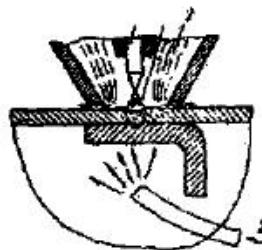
Дуговая точечная сварка в среде инертных газов 1-дуга; 2- инертный газ; 3-вольфрамовый электрод
